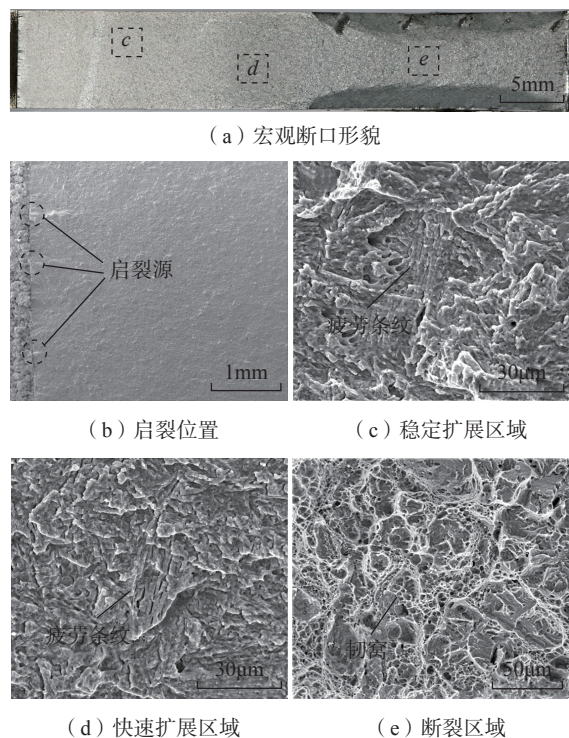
30CrMnSiNi2A 超高强度钢电子束焊接头焊缝区疲劳裂纹扩展速率试样的断口形貌
